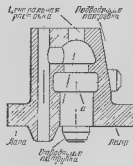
Корпус блока парораспределения (корпус показан в рабочем положении; формовка отливки производится в переворотном положении).
